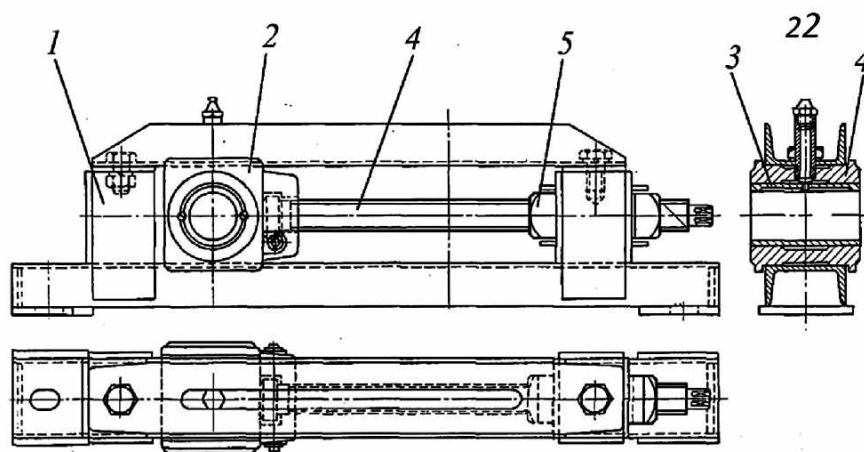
Гвинтовий натяжний пристрій: 1 – корпус; 2 – повзун; 3 – вкладиш; 4 – гвинт; 5 – гайка
